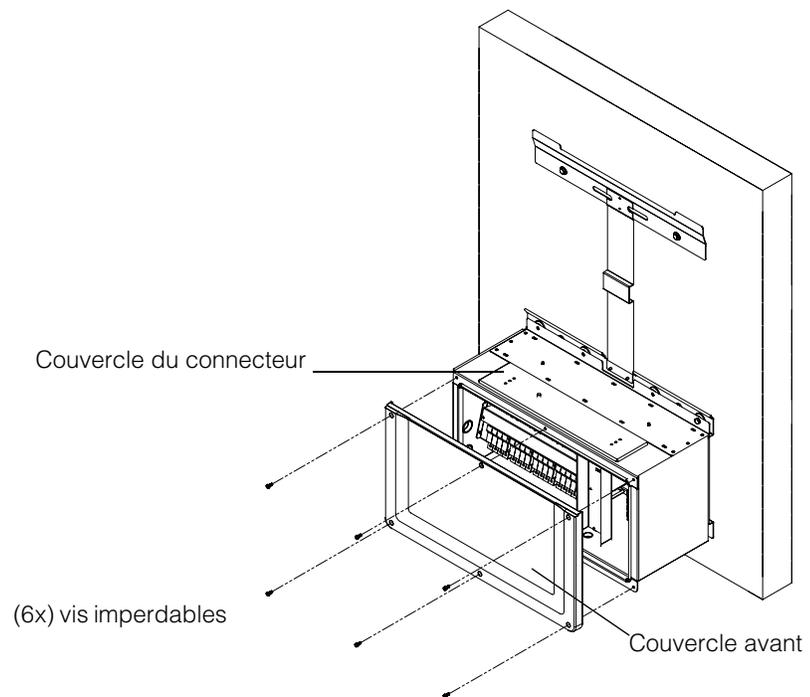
Ouverture du couvercle avant du boîtier de câblage
